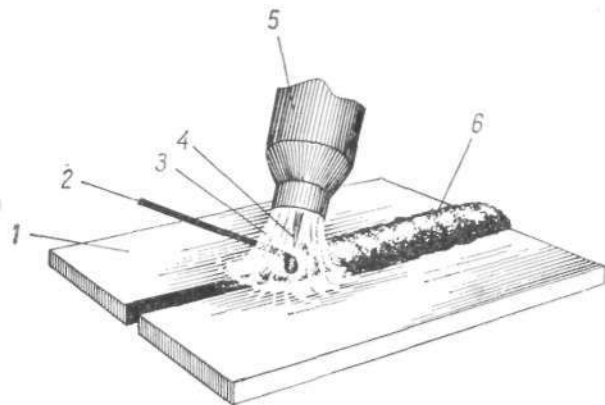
Схема аргоно-дуговой сварки.
